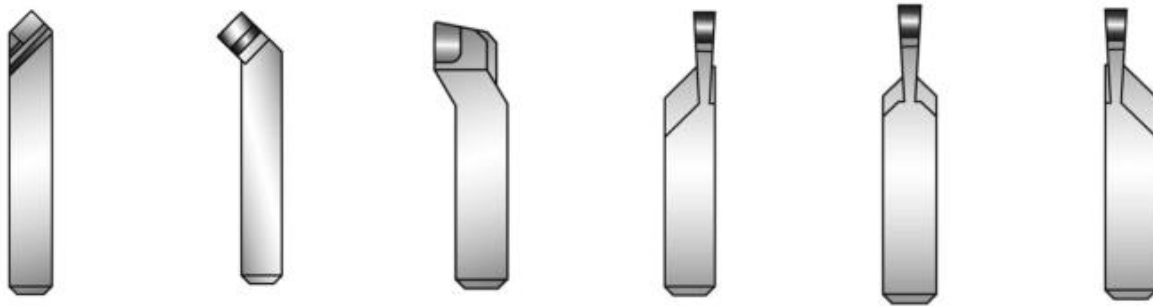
Классификация резцов по конструкции рабочей части
